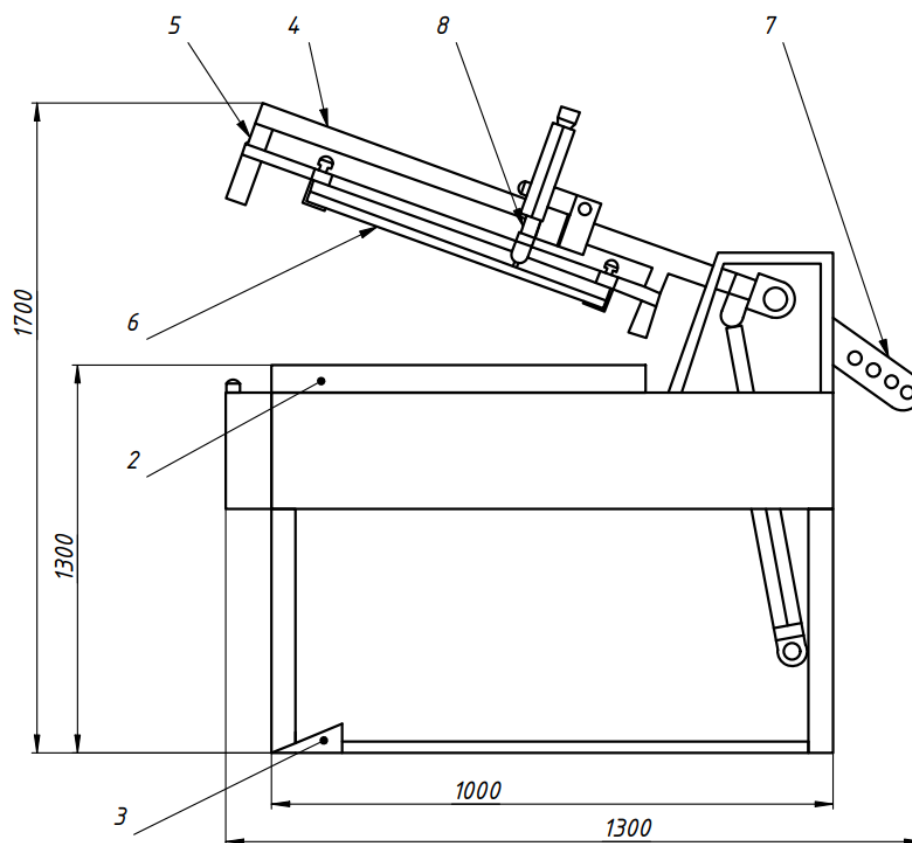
Схема напівавтоматичної друкарської машини (вид збоку)
